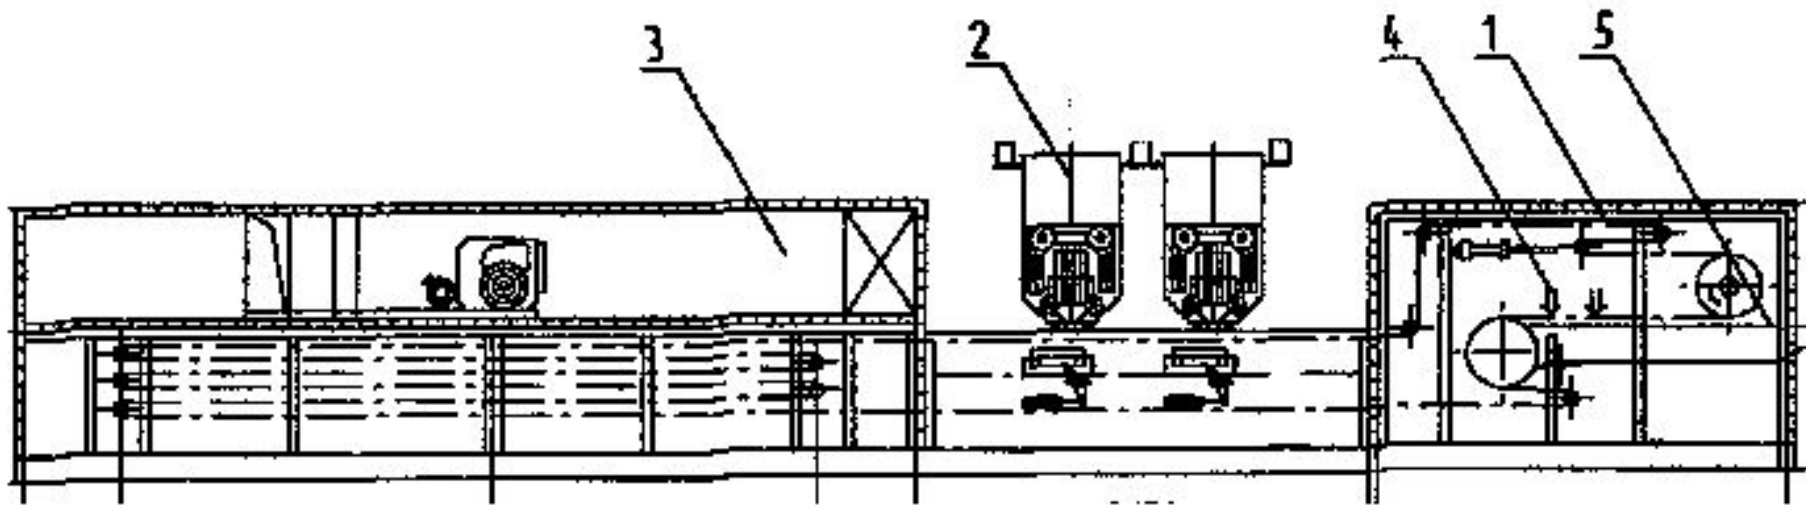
Агрегат фирмы «Винклер и Дюннебир» для отливки корпусов конфет в силиконовые формы
